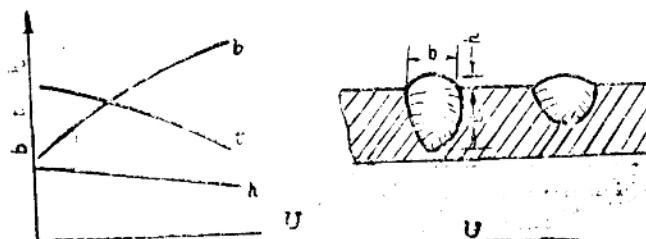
1—5 焊接电压U对焊缝形状的影响
